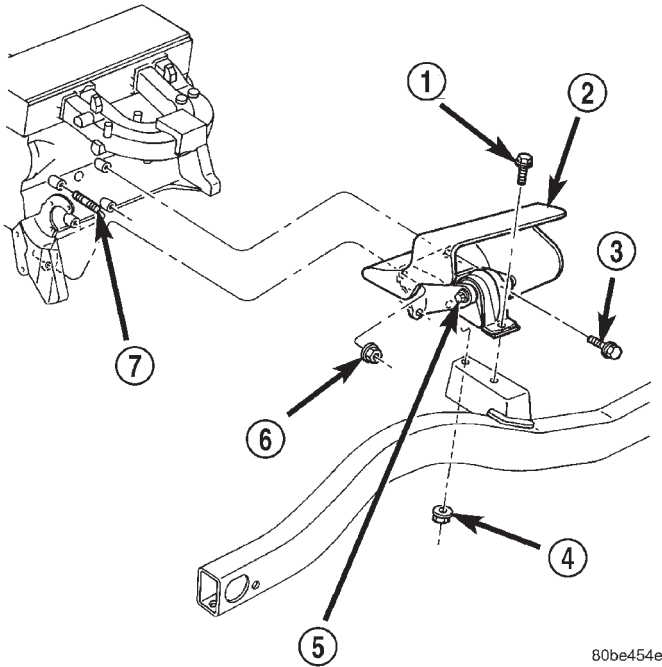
Soporte delantero izquierdo – motor 2.5L
